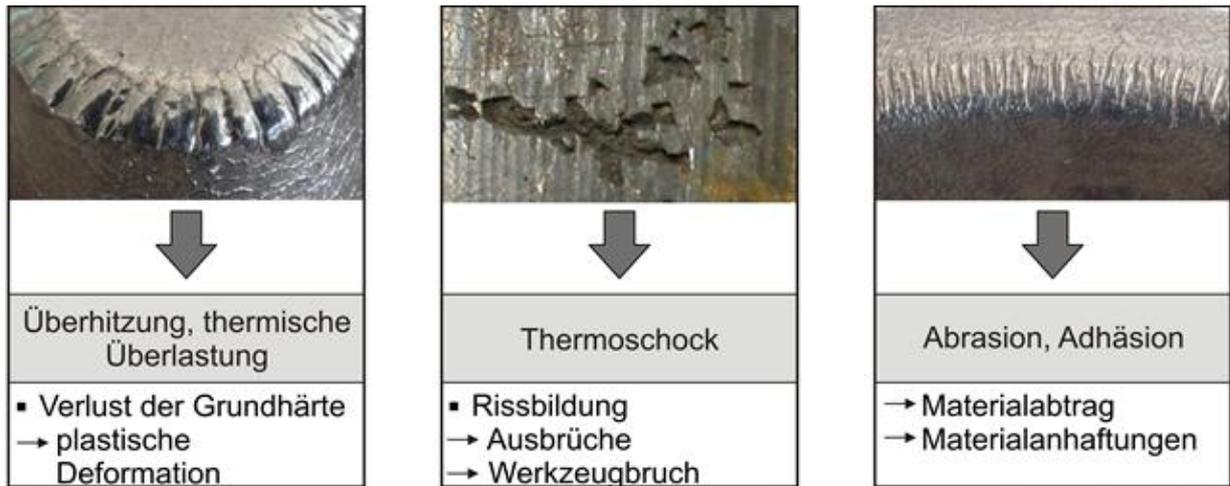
Ursachen und Hauptversagensmechanismen an der Oberfläche von Schmiedewerkzeugen
